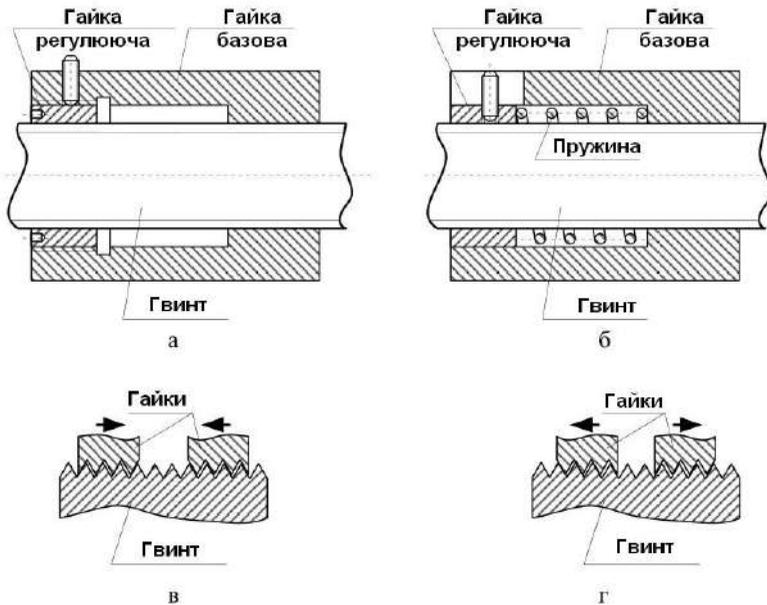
Схема люфтоусуваючого механізму на основі гайки із твердим і пружним регулюванням осьового зазору
